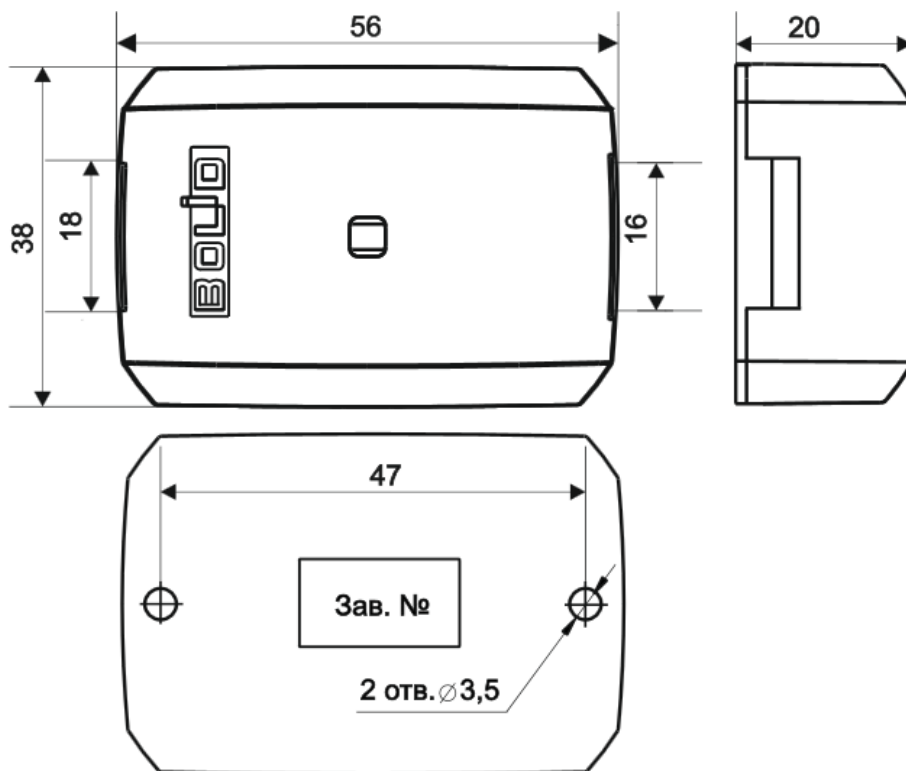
Габаритные и установочные размеры корпуса «C2000-WiFi»
